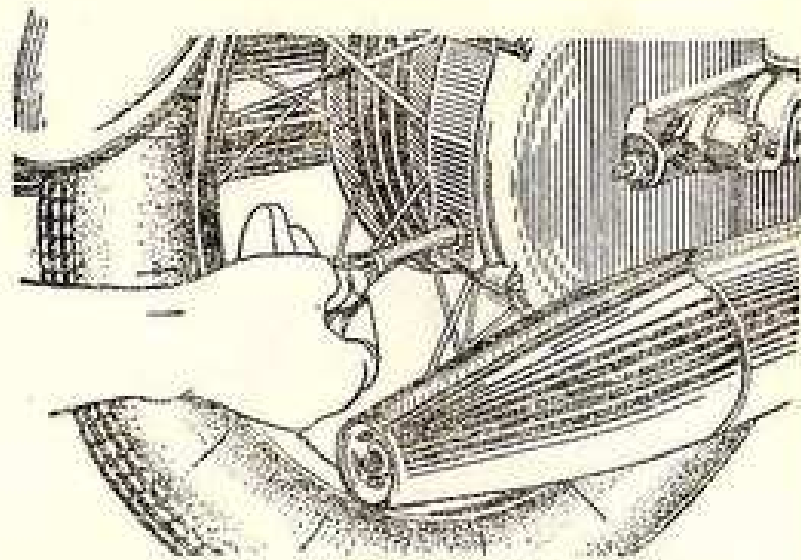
РЕГУЛИРОВКА НОЖНОГО ТОРМОЗА
